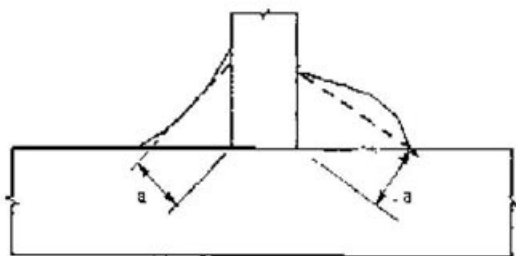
Épaisseur de la soudure en angle
